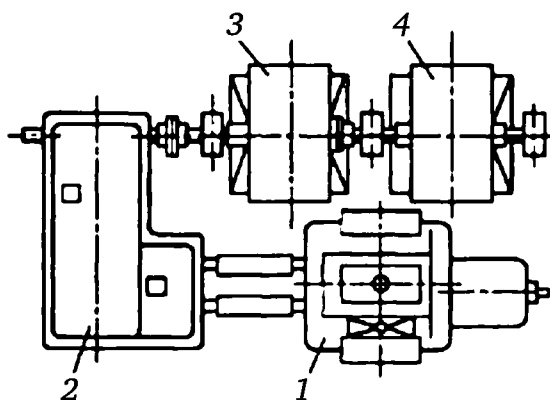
Привод пластосмесителя с двумя электродвигателями
